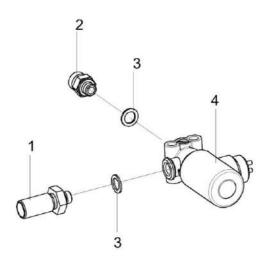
Клапан электромагнитный КВК-2-0801060 и КВК-2-0801060-02
